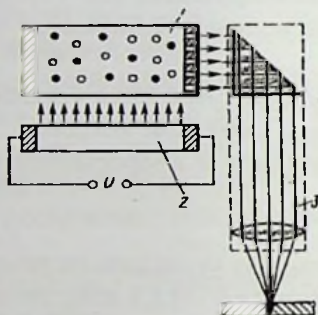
Схема установки для лазерной сварки с твердотельным лазером:
